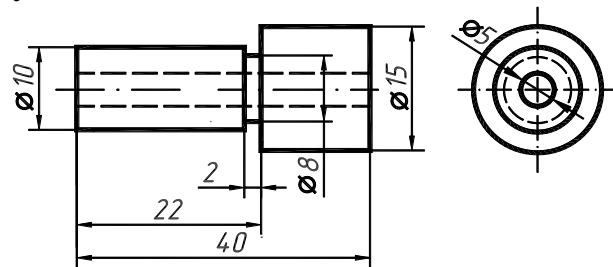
Приклад використання умовної позначки \varnothing для нанесення розміру на кресленикові деталі, що має циліндричну форму
